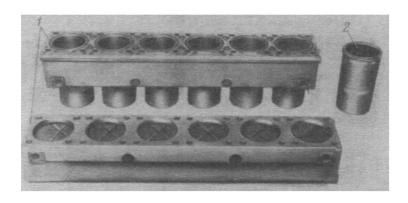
Блок цилиндров: 1—блок цилиндров: 2—гильза
